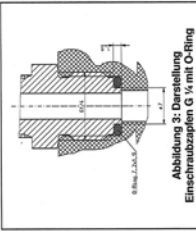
Querschnitt einer Einschraubbohrung G 1/4 mit O-Ring
